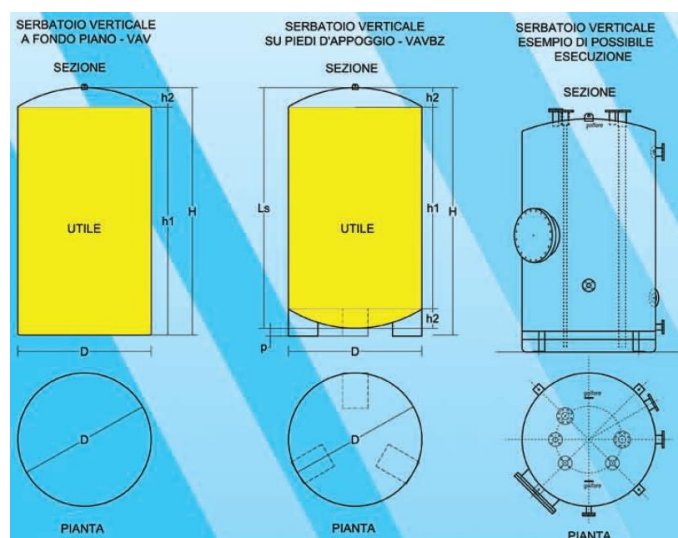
TIPOLOGICO SERBATOIO VERTICALE IN ACCIAIO CON SEZIONI E PROSPETTI.
